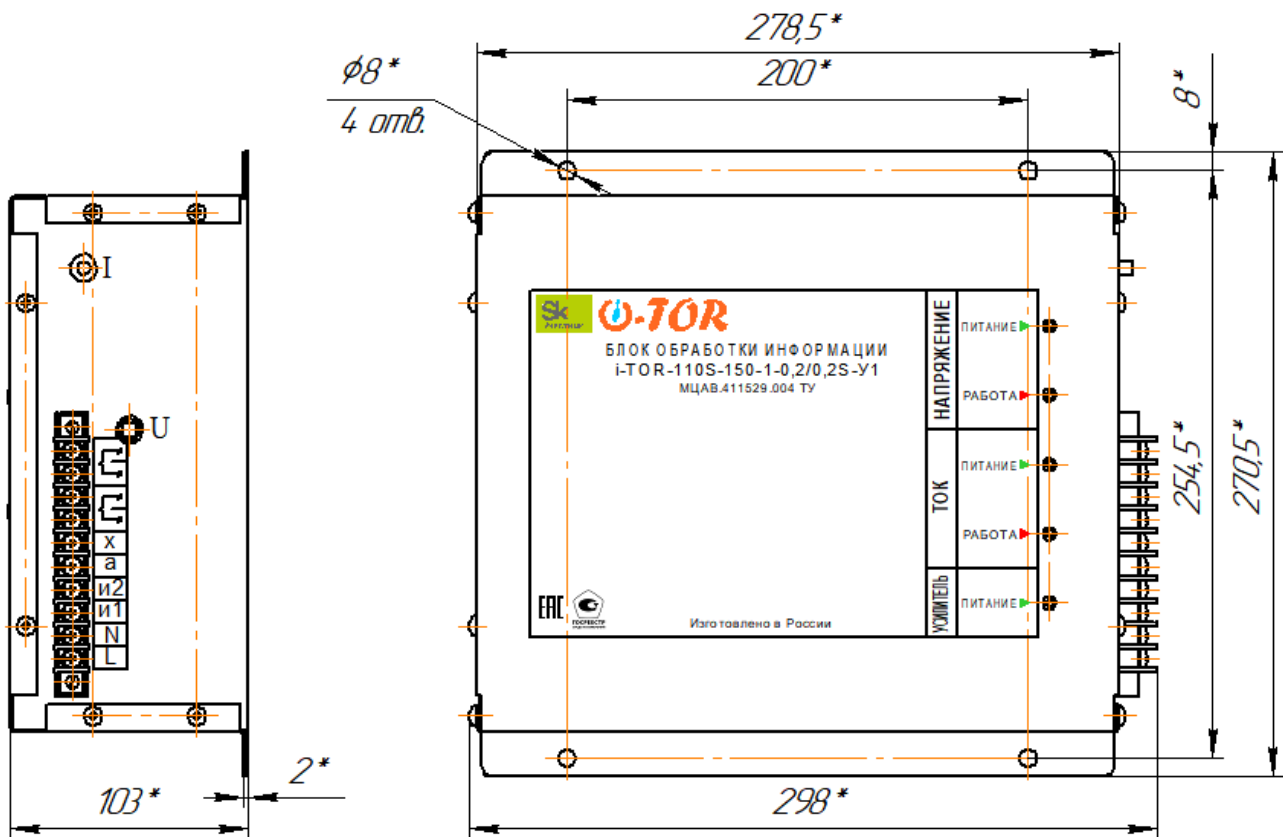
Е – габаритно-установочные размеры блока обработки информации I-TOR-110S
